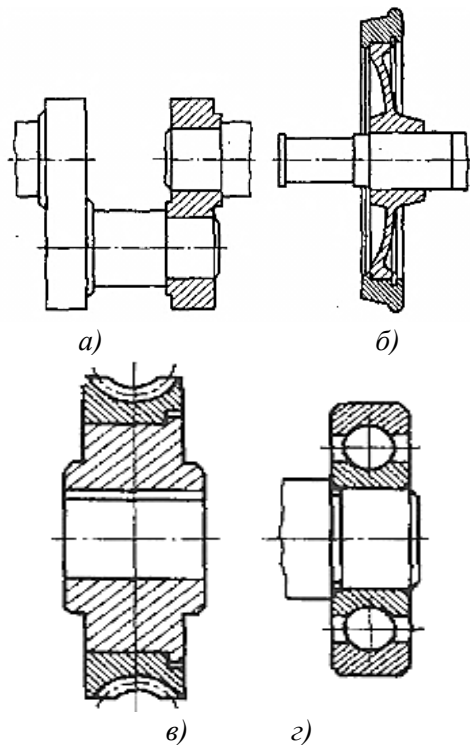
Соединения с натягом по цилиндрическим поверхностям
